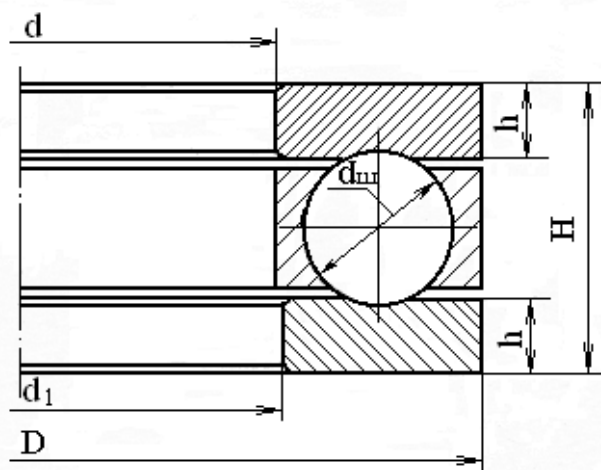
В.9 – Подшипник шариковый упорный, однорядный
